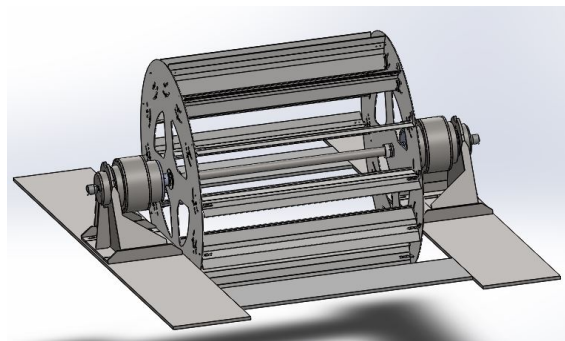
Wasserrad mit mechanisch geteiltem Generator
